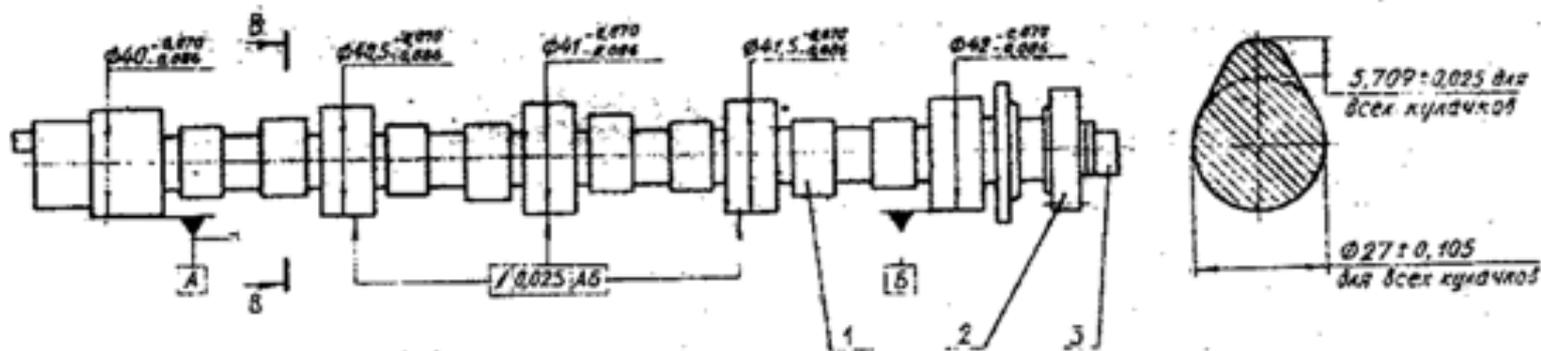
Вал распределительный в сборе: 1 - вал распределительный; 2 - шестерня; 3 - кулачок привода бензинового насоса
